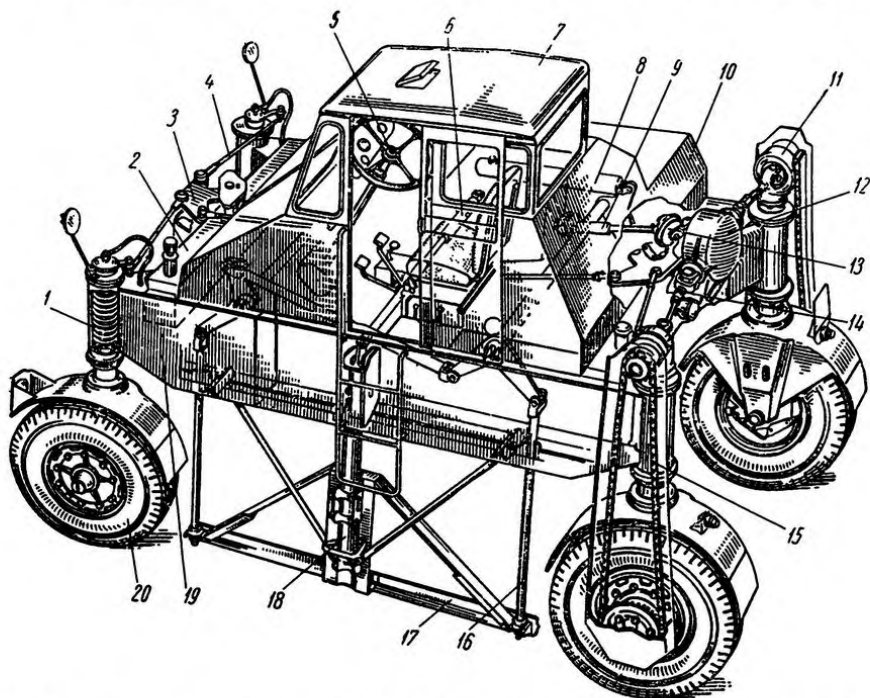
Конструктивная схема порталного автомобиля с четырьмя управляемыми поддрессоренными колесами:
